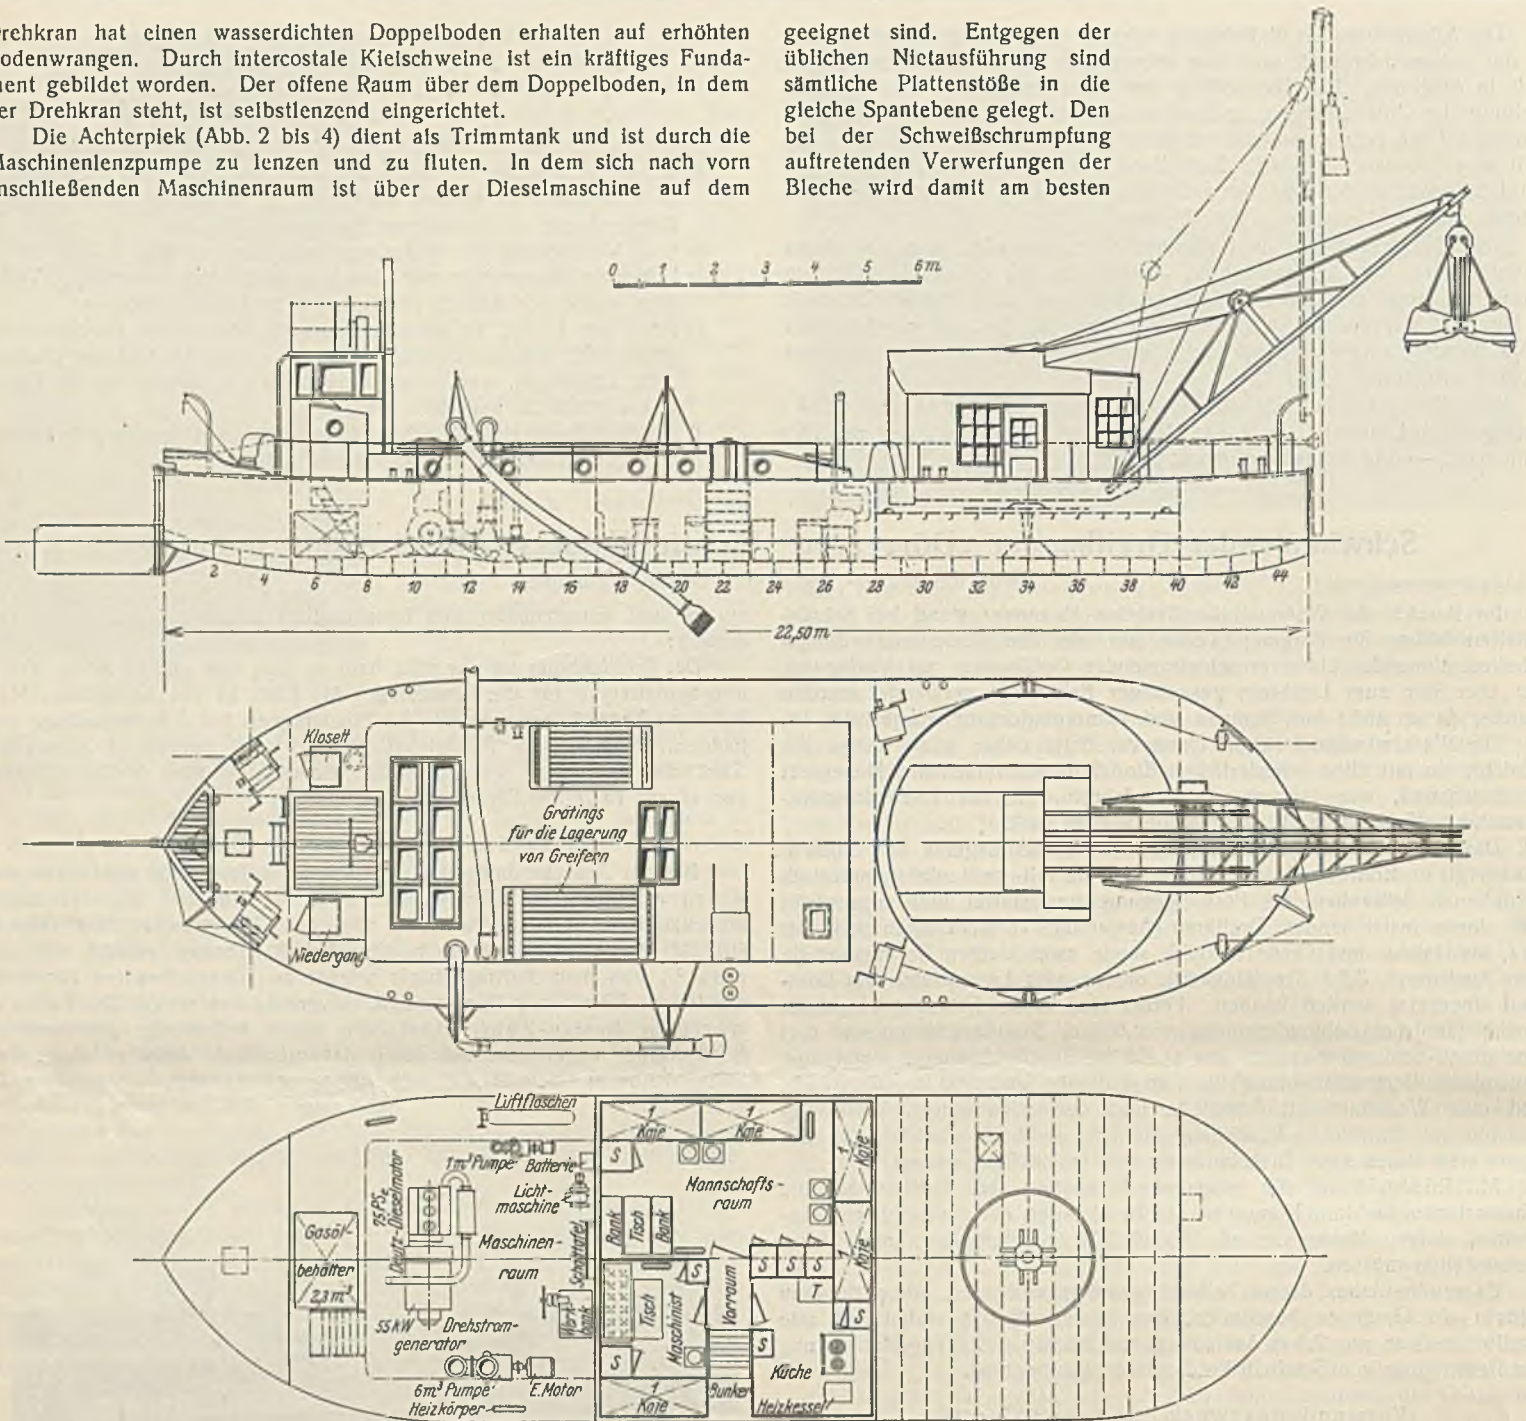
bis 4. Ansicht, Deckplan und Stauplan.
